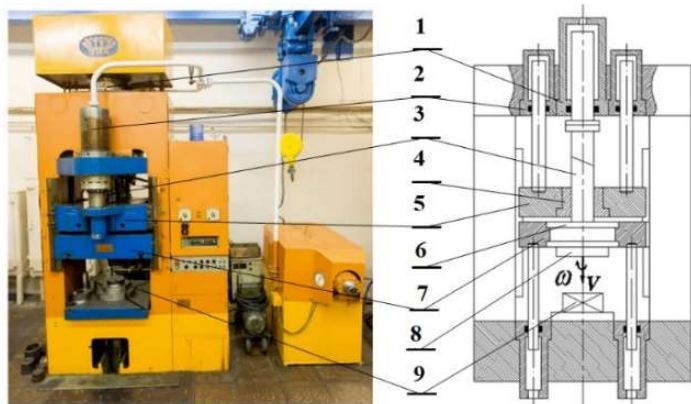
Общий вид (а) и схема (б) гидравлического пресса для штамповки с кручением (1- цилиндр центральный; 2 – цилиндр для вращения; 3 – винта; 4 - гайка; 5, 7 – ползун 6 – штамподержатель; 8 – инструмент; 9 - заготовка; V - скорость осевого перемещения инструмента; ω - скорость вращения инструмента)
